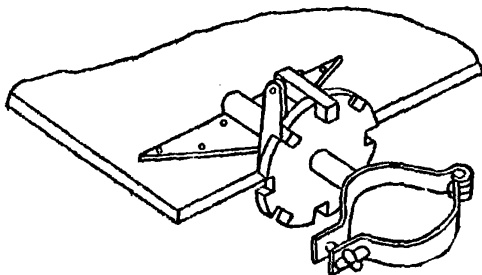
Приспособление К. Г. Козлова для сборки узлов
